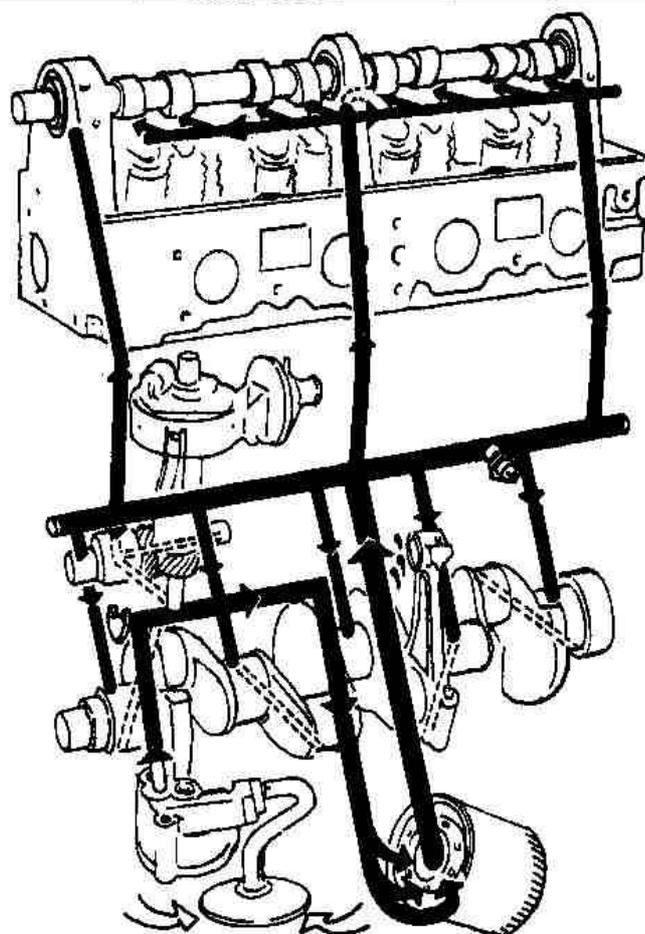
Б.4. Циркуляция смазки в двигателе (Разд. 24)
